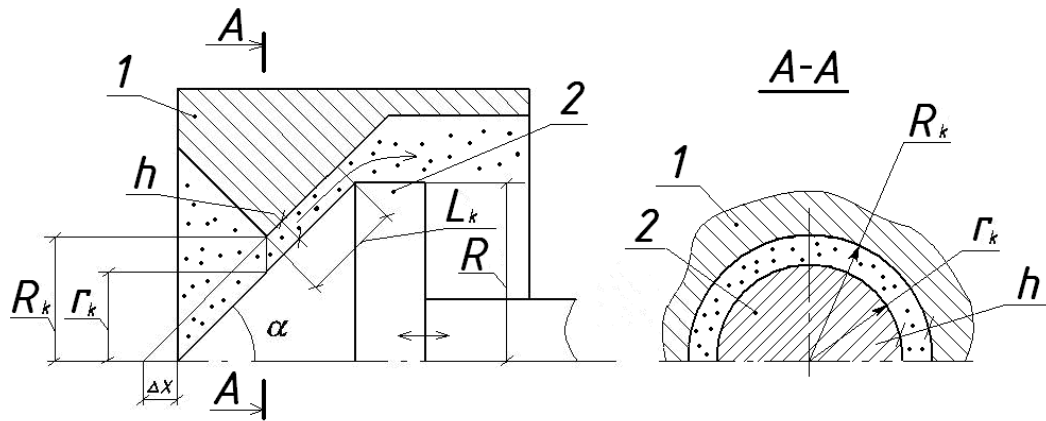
Робоче положення головки експандера на початку роботи: 1 – поверхня корпусу експандера; 2 - конус головки експандера, який закриває робочу поверхню корпусу.
